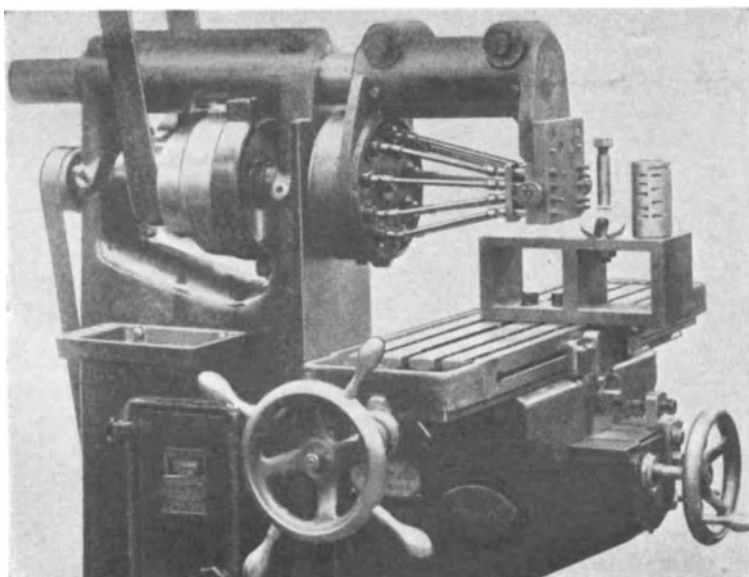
Mehrspindelfräsmaschine aus Ständerfräsmaschine umgebaut.
